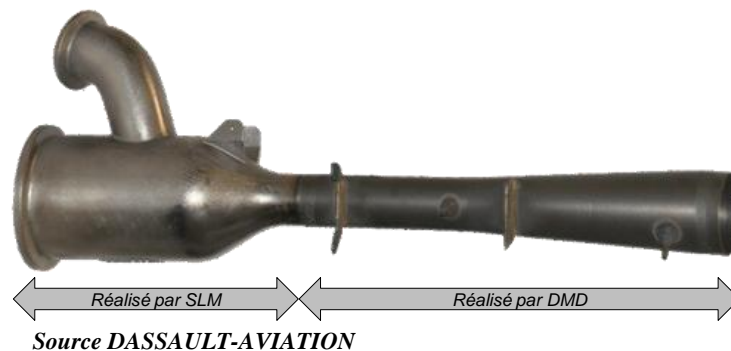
Démonstrateur monobloc de grande dimension (mélangeur air chaud / air froid de 700 mm de long) réalisé conjointement par SLM et DMD
